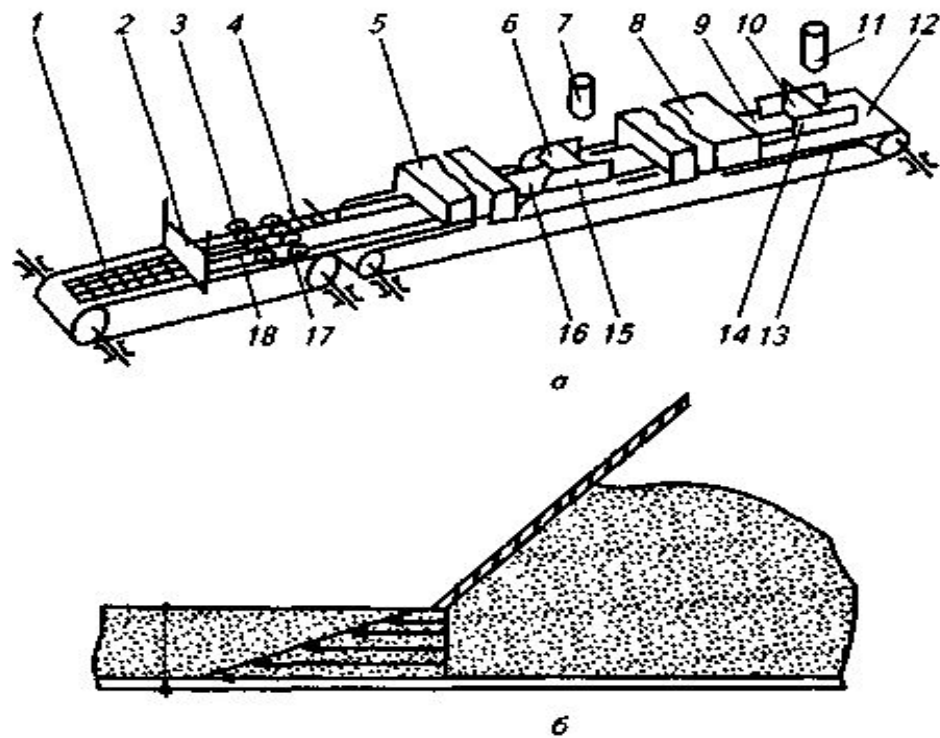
Схема формирования конфетных корпусов размазкой и резкой (а - общая схема, б - схема размазки)
